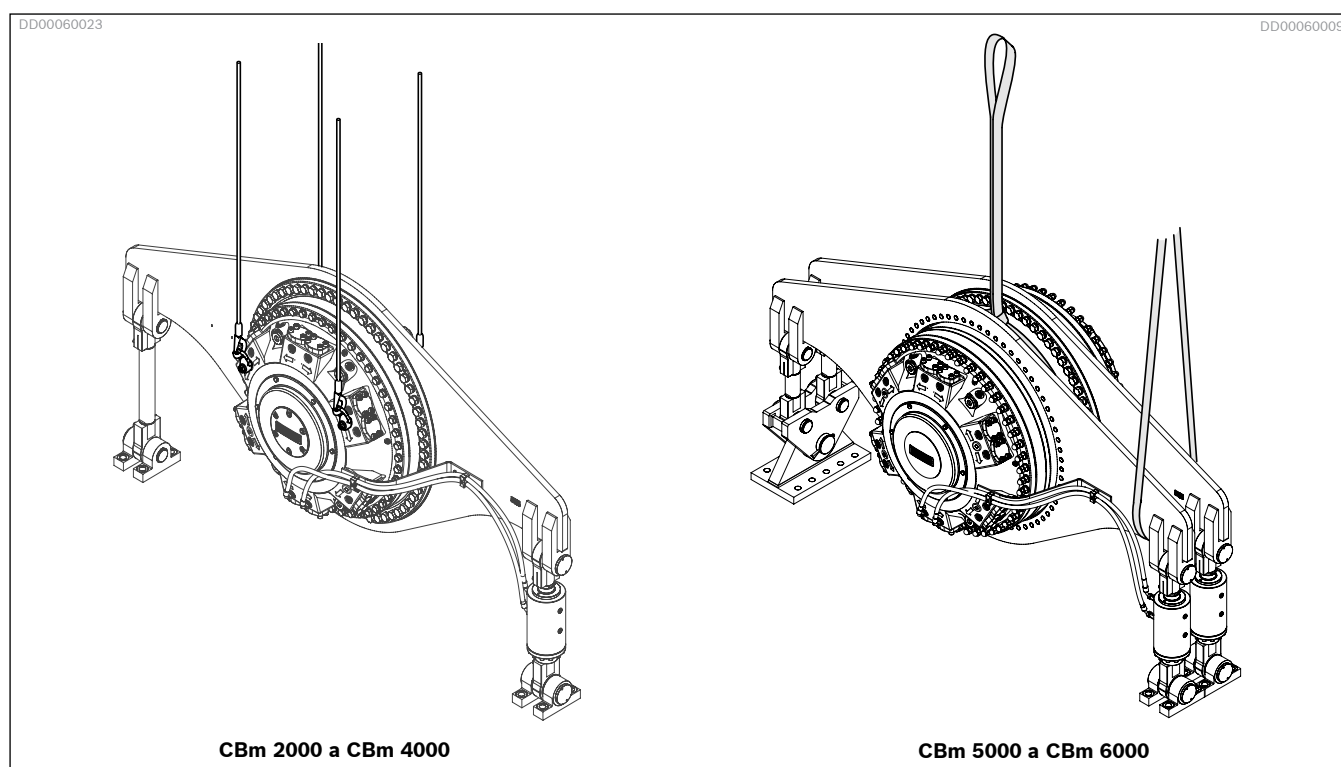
Elevação do motor e braço de torque de duas terminações montado
